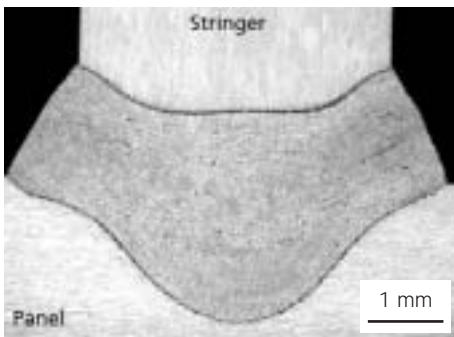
Querschliff einer beidseitig gleichzeitig geschweißten Panel-Stringer-Verbindung im T-Stoß
